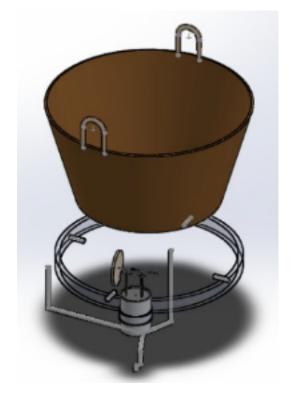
Modelado Conjunto motor y soporte de motor, sin hornos.
